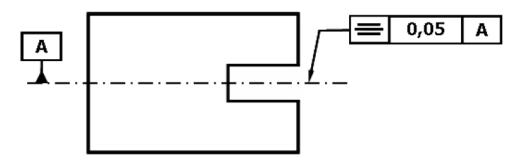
Indicação de tolerância de simetria em desenho técnico
